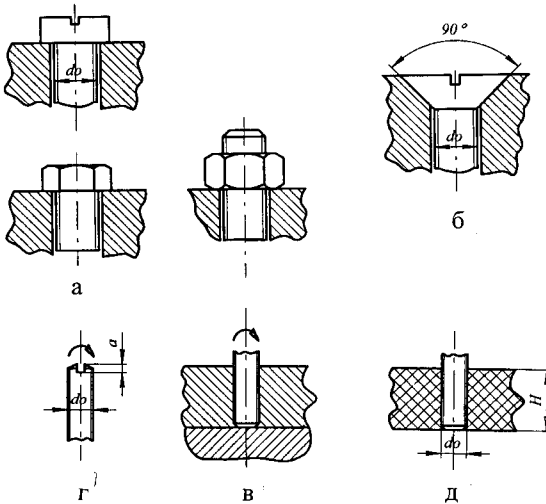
Різьбові з'єднання для визначення моменту затяжки: а – контактування головки болта чи гайки з деталлю по плоскій поверхні; б – по кінчній поверхні з кутом 90°; в – загвинчування шпильок чи болтів, які упираються торцем стержня; г – загвинчування установчих гвинтів; д – схема для випадку, коли різні механічні властивості гвинта і гайки.
